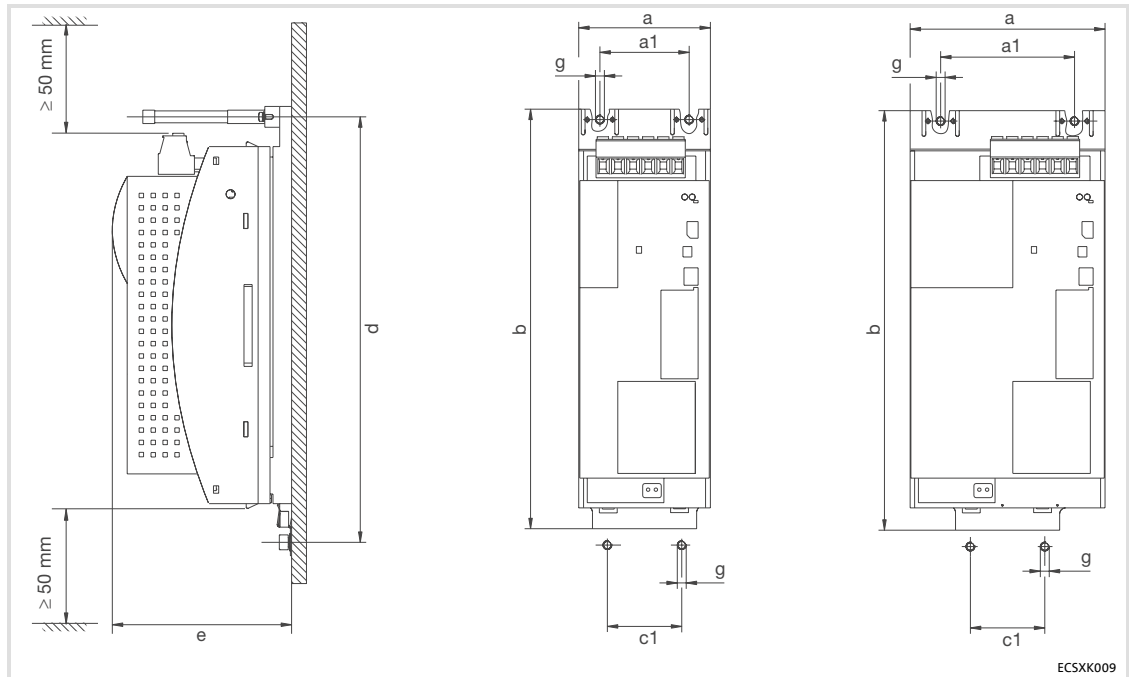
Abmessungen bei Montage in "Cold Plate"-Technik, Typ ECSCKxxx
